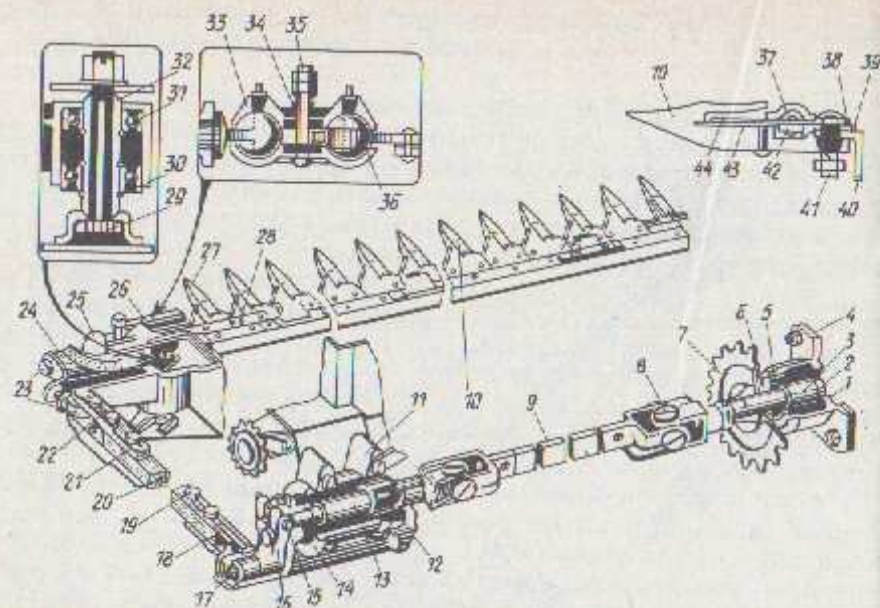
Режущий аппарат и механизм привода ножа:
